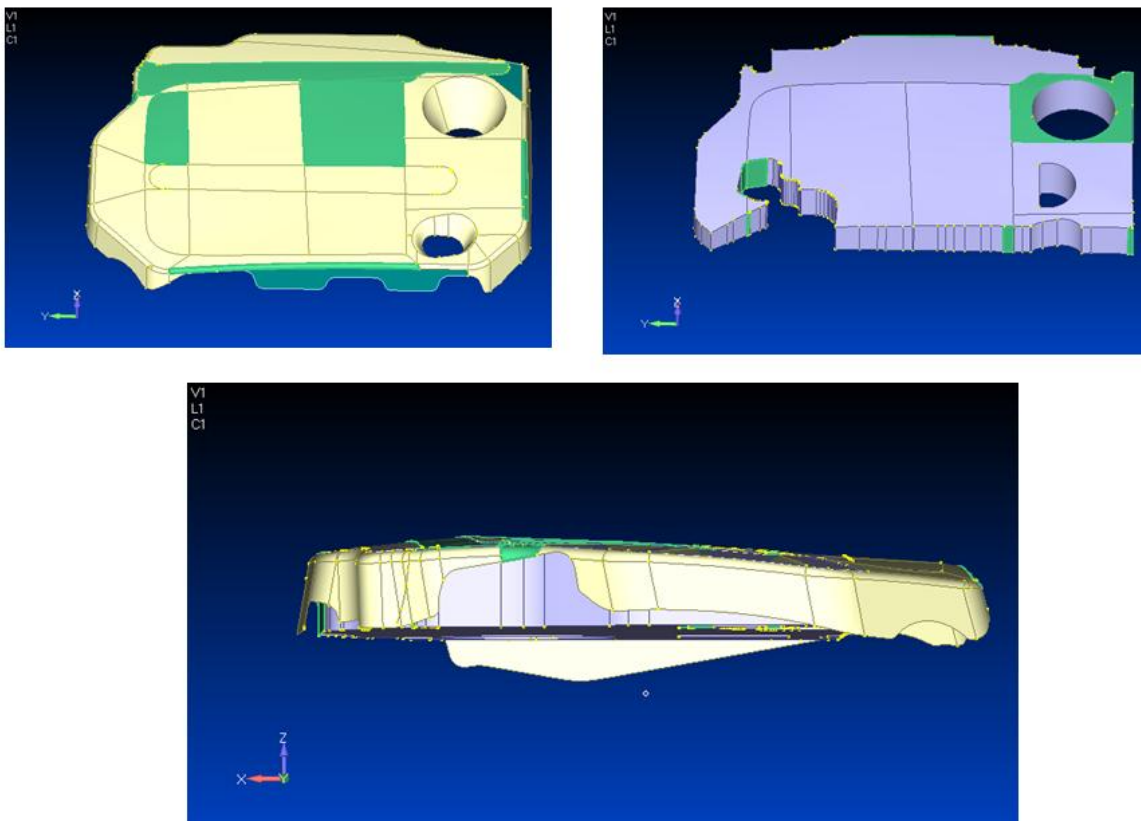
Geometrie CAD del componente in plastica (in alto a sinistra) e del componente di poliuretano (in alto a destra).
